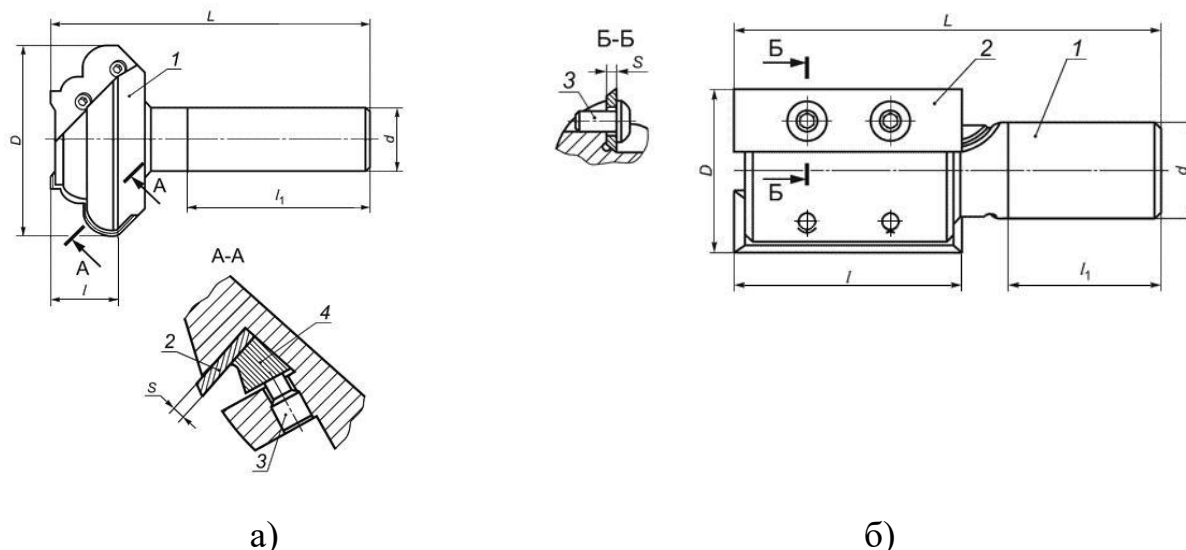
Фрезы концевые с механическим креплением сменных режущих пластин для обработки древесины и композиционных древесных материалов по ГОСТ Р 53926-2010:
